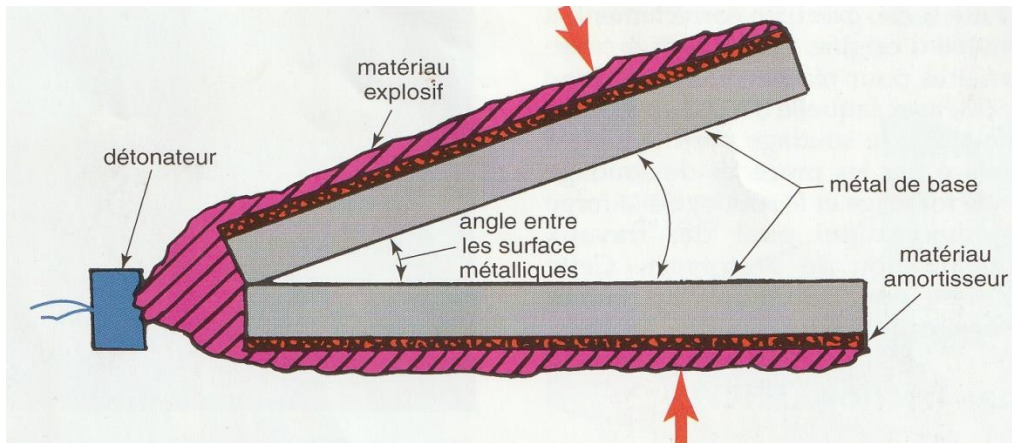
Diagramme schématique d'un montage de soudage par explosion [13].
